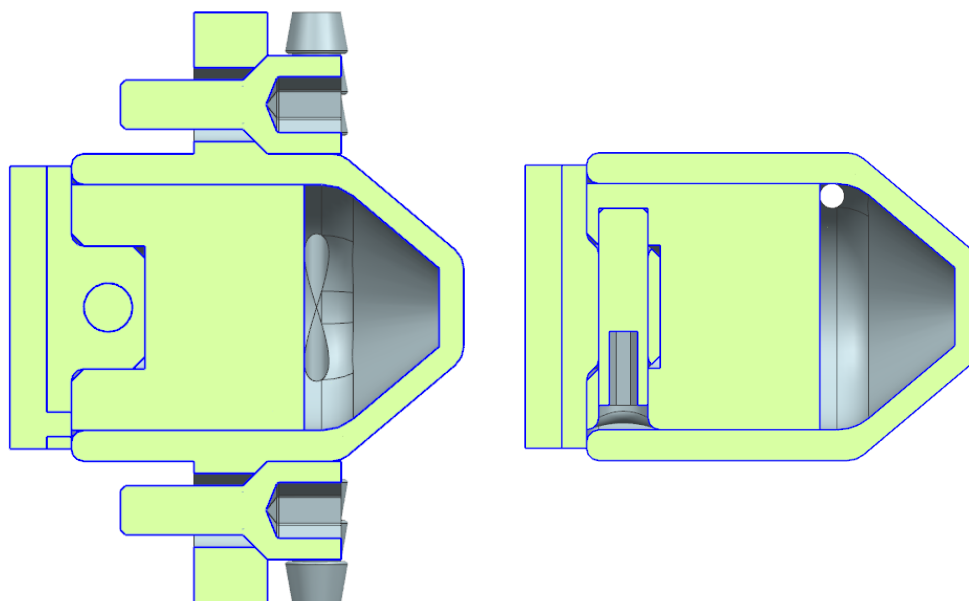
Popis sestavy hydraulického třmenu s postupem montáže
